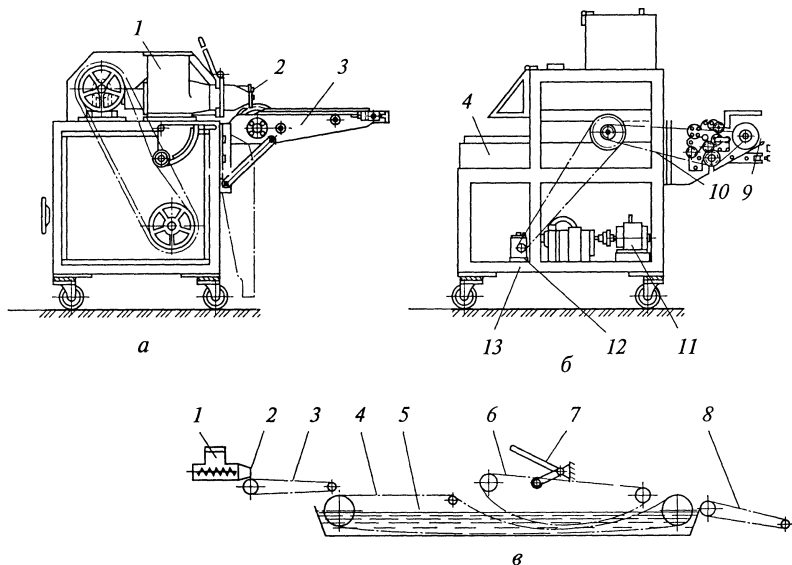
Агрегат для формования и обварки тестовых заготовок соломки:
